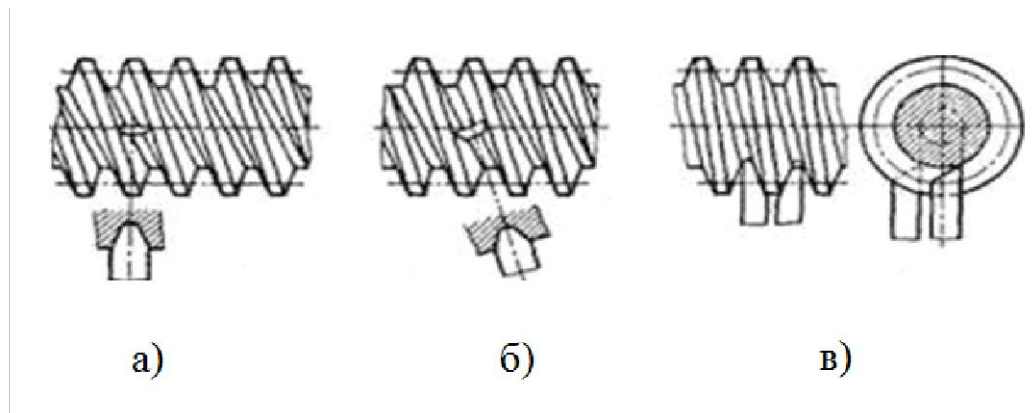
Классификация червячных передач по форме боковой (рабочей) поверхности витка червяка
